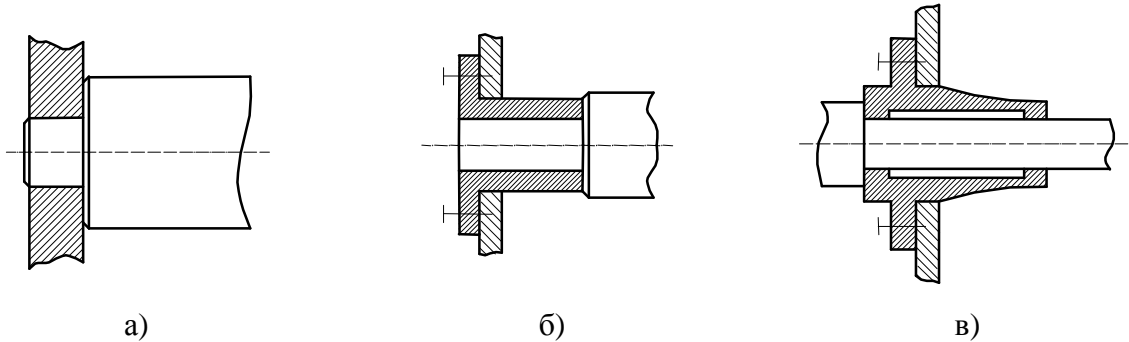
Опори з тертям ковзання: а – опора ковзання; сприймає осьові навантаження, виконується в товстому корпусі; ремонт ускладнений; б – опора з підшипниковою втулкою для тонкостінних корпусів; легко замінюється; в – підшипникова втулка; більша твердість при консольному закріпленні валу
